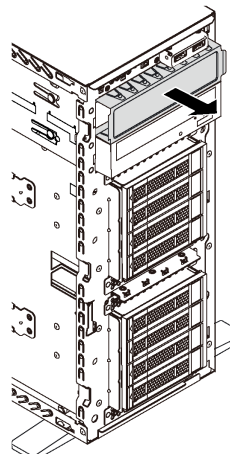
Entfernen der Abdeckblende für die Laufwerkposition
